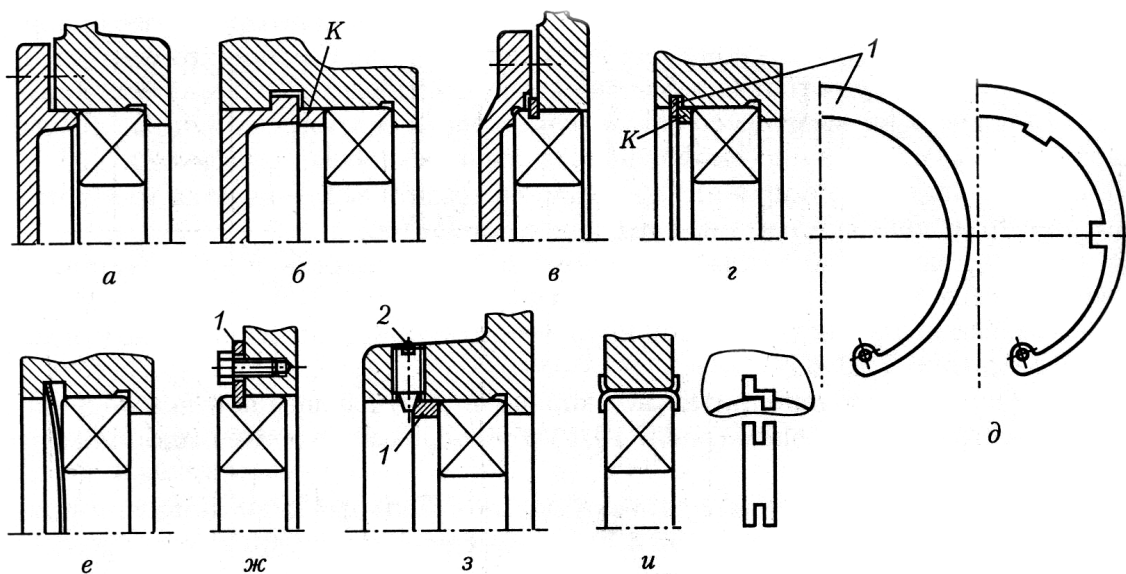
Способы крепления подшипников качения в корпусе:
